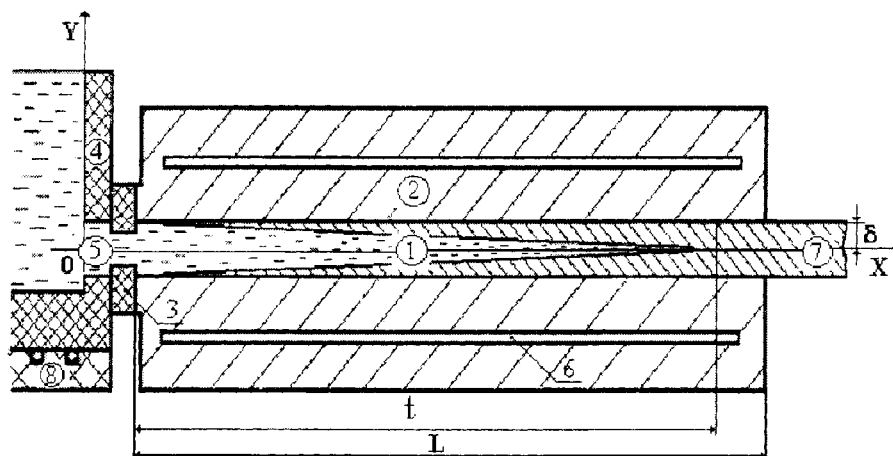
Расчетные области задачи: 1 – отливка; 2 – кристаллизатор; 3 – соединительный стакан; 4 – стенка металлоприемника; 5 – отверстие питателя; 6 – канал водяного охлаждения; 7 – цинковая полоса; 8 – нагреватель;  $t$  – шаг вытяжки;  $L$  – длина кристаллизатора;  $\delta$  – половина толщины отливки
